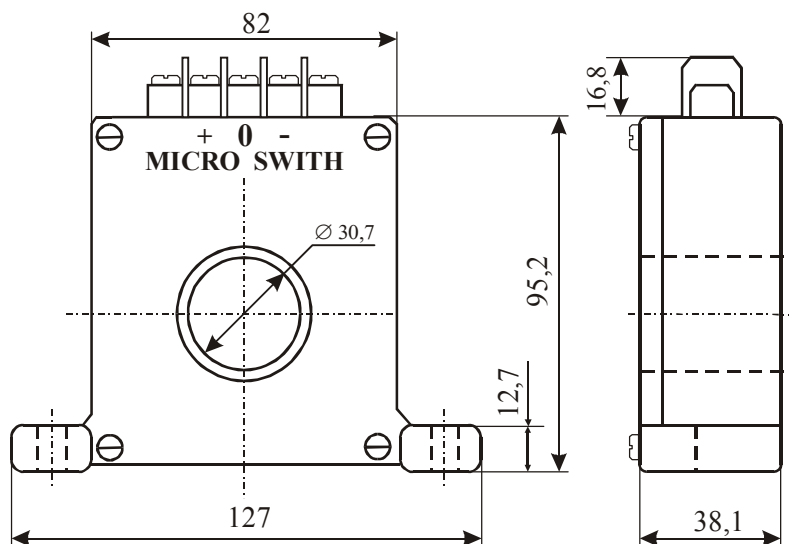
Внешний вид и габаритные размеры датчиков тока серий CSLE и CSLF, размещенных в металлическом корпусе
